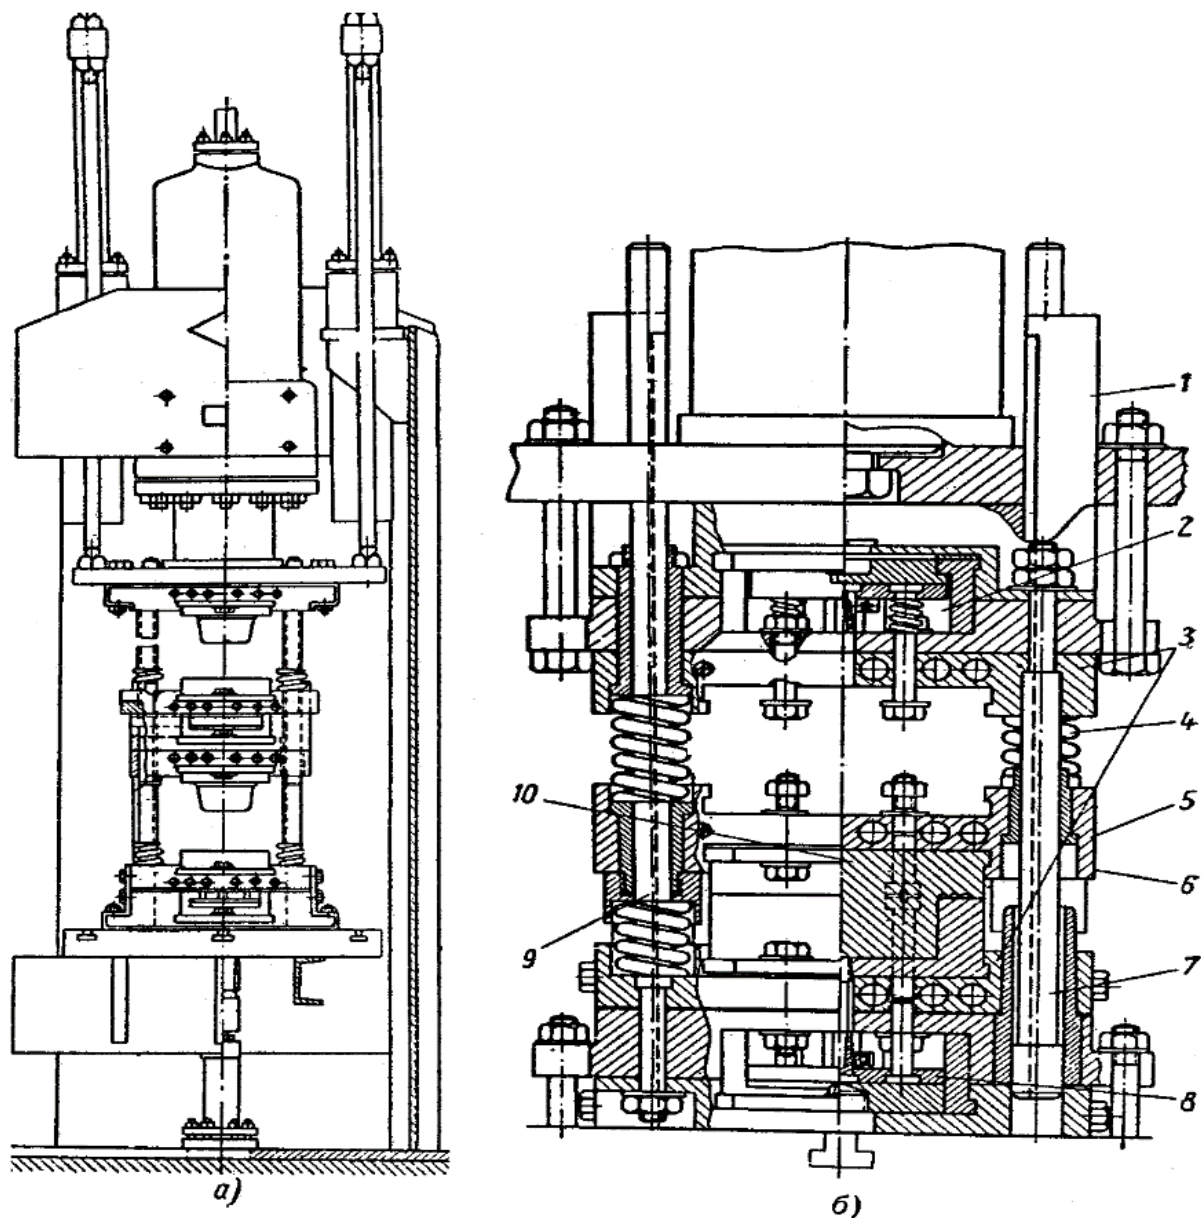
Гидравлический пресс с инструментальной оснасткой для двухэтажного прессования: *а* – общий вид пресса; *б* – оснастка для двухэтажного прессования; 1 – тяговое устройство; 2 – выталкиватель; 3 – верхняя и нижняя плиты обогрева пресс-форм; 4 – буферная пружина; 5 – промежуточная греющая плита; 6 – теплоизоляция; 7 – направляющая колонка; 8 – нижний выталкиватель; 9 – направляющие колонки; 10 – оформляющее гнездо
